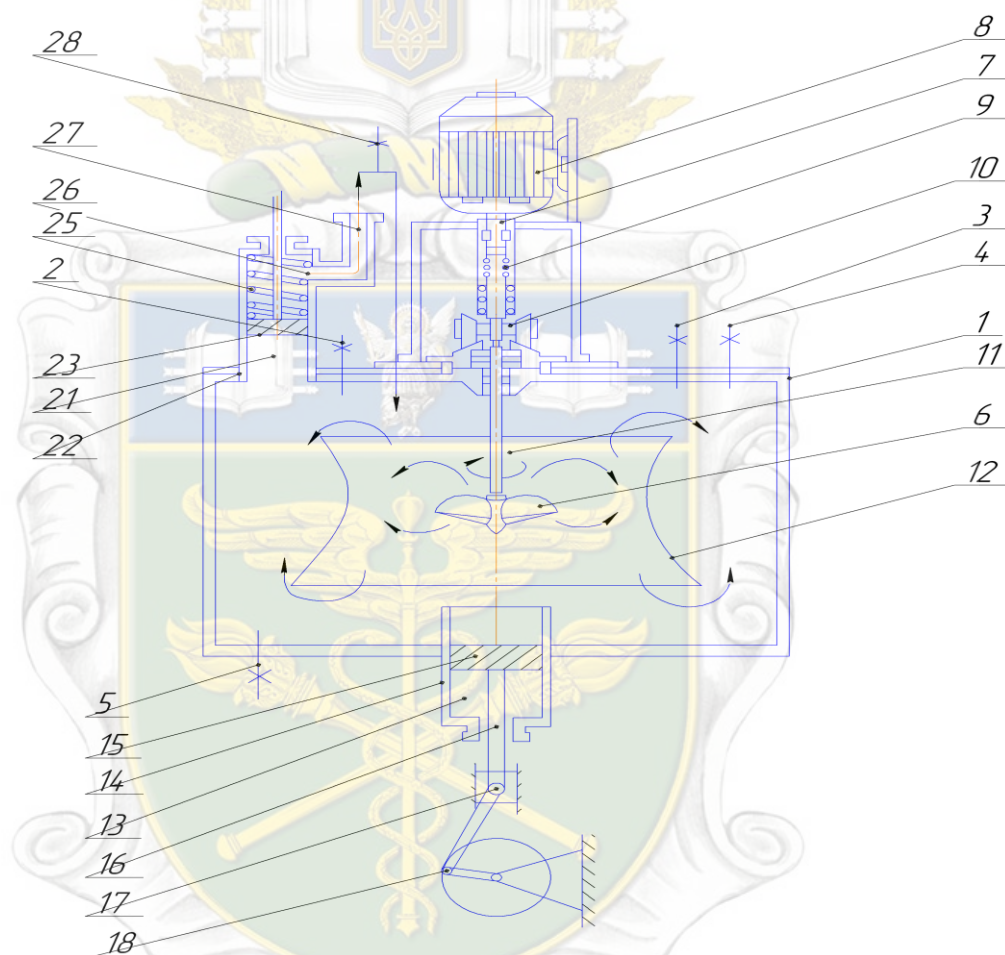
Мішалка резервуару В2-ОХР
